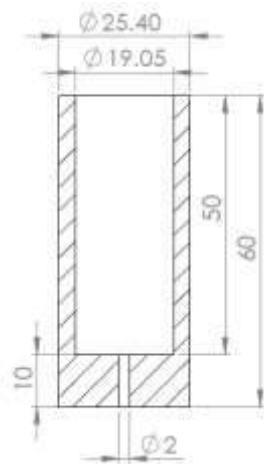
Diseño de crisol #1 para fundición (cotas en mm)
